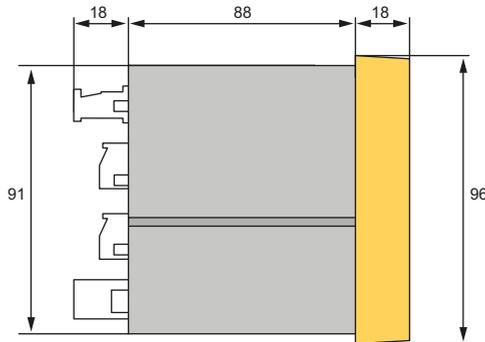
Maßbild PEM575 (Seitenansicht)
